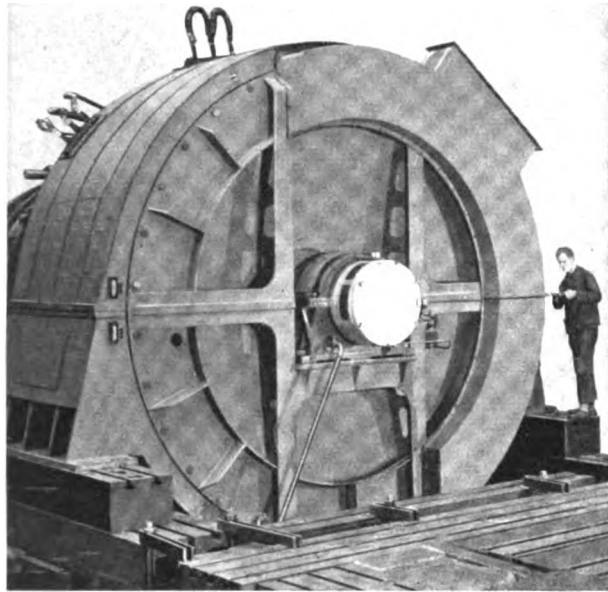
Schiffsschraubenmotor, 9600 kW, 160 U/min.
